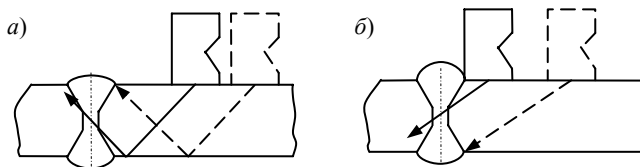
Схемы контроля стыковых сварных соединений:
